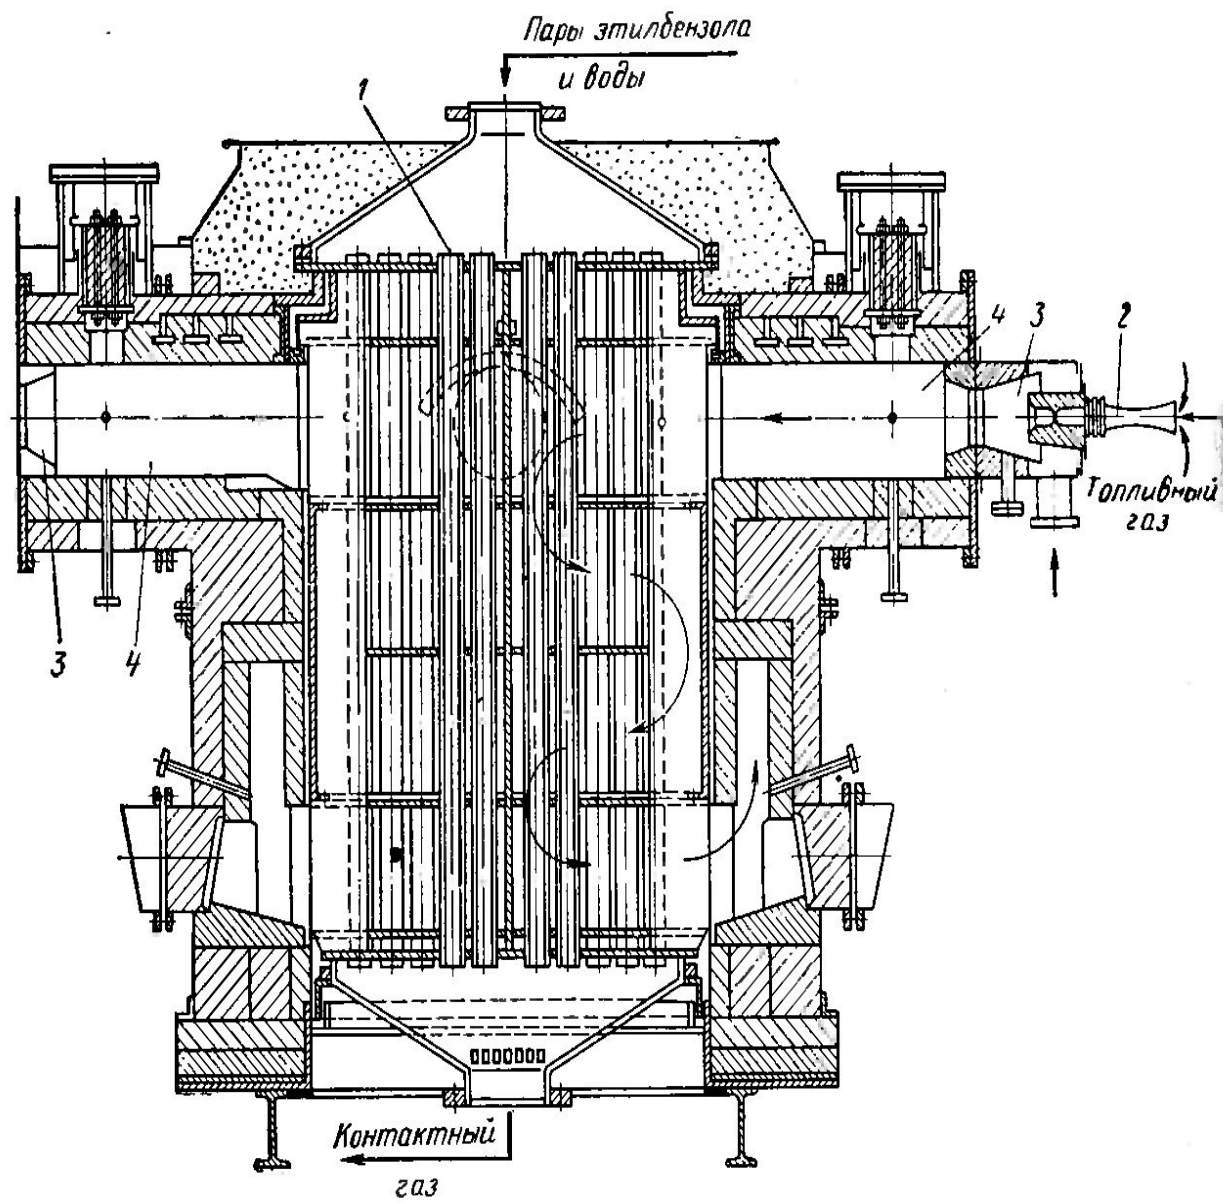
Трубчатый реактор с обогревом дымовыми газами
